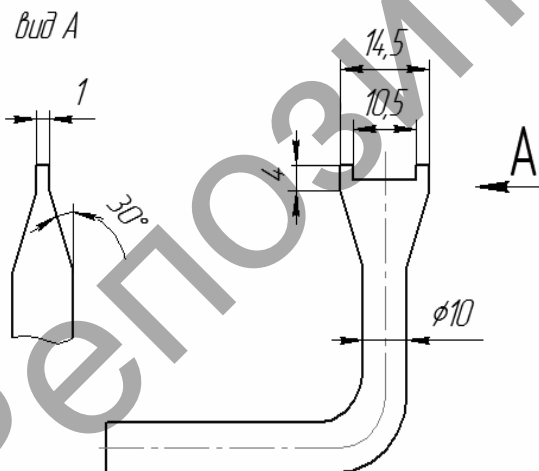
Специальная отвертка для разборки и сборки клапанов бустера.
